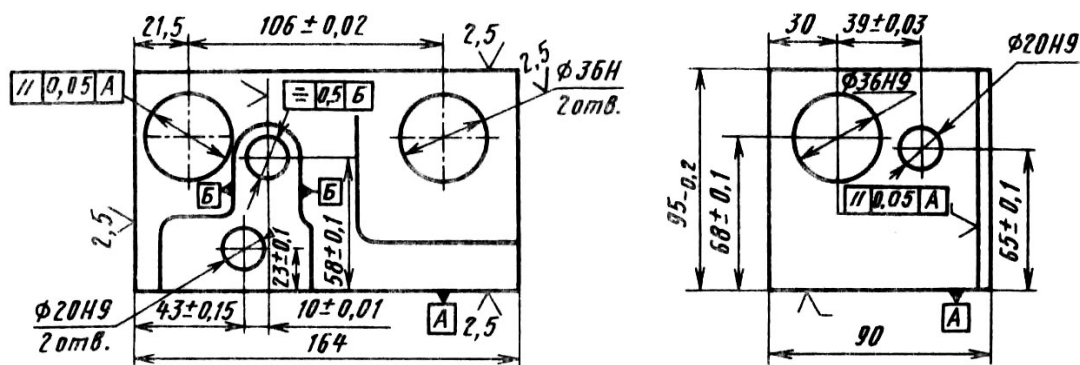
Эскиз корпусной детали, предназначенной для обработки на автоматизированном участке
